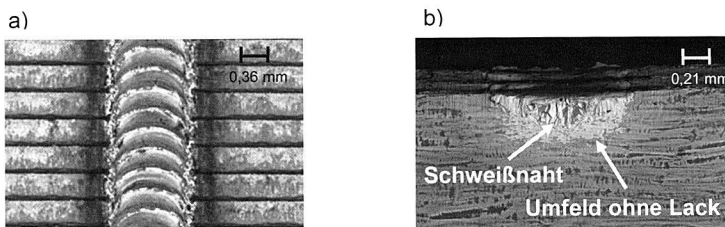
Blechpaket mit Schweißnaht; a) Oberflächenansicht, b) Querschnitts-Ansicht
